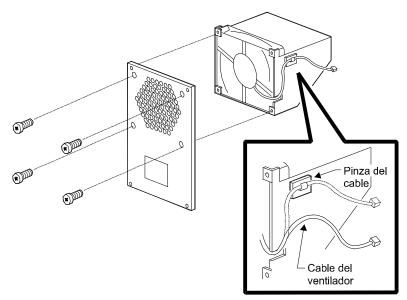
Extracción del cable del ventilador y de los tornillos del conjunto de ventilador
